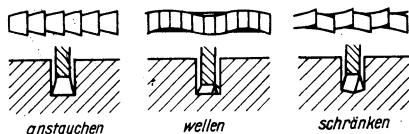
Verschiedene Zahnformen der Metallsägeblätter
